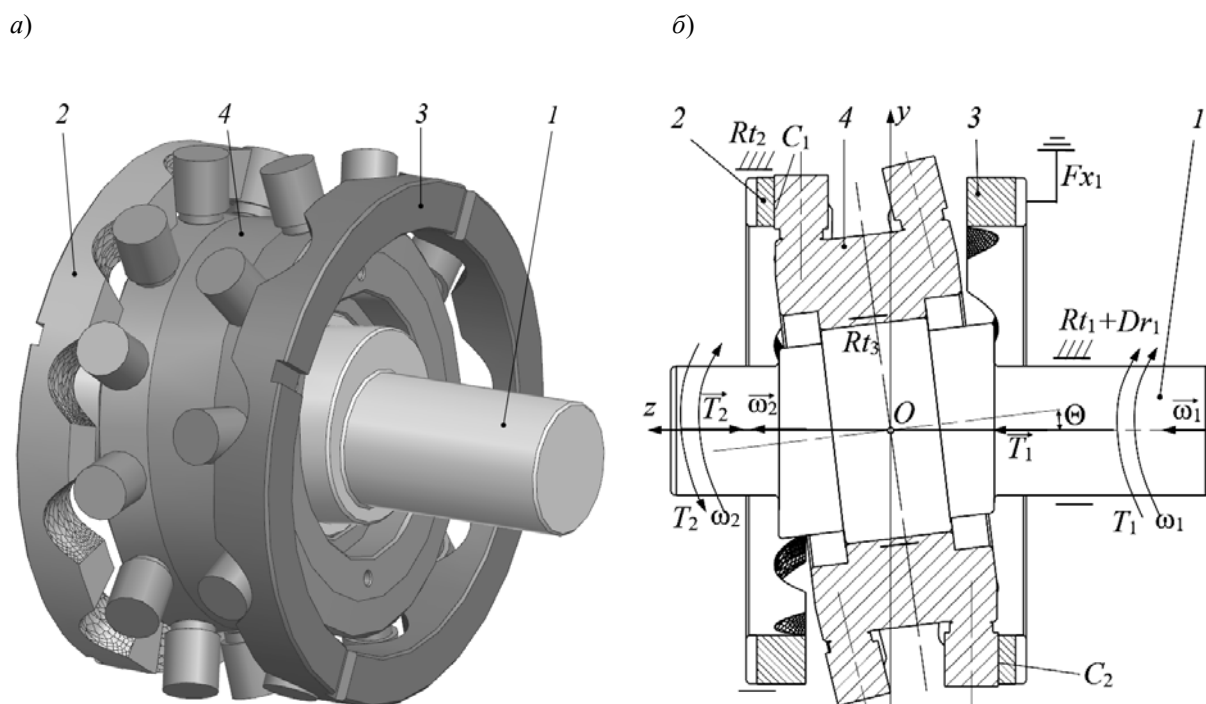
Модель СРП с двухрядным сателлитом: а – общий вид; б – с обозначением шарниров, контактов и нагрузок
